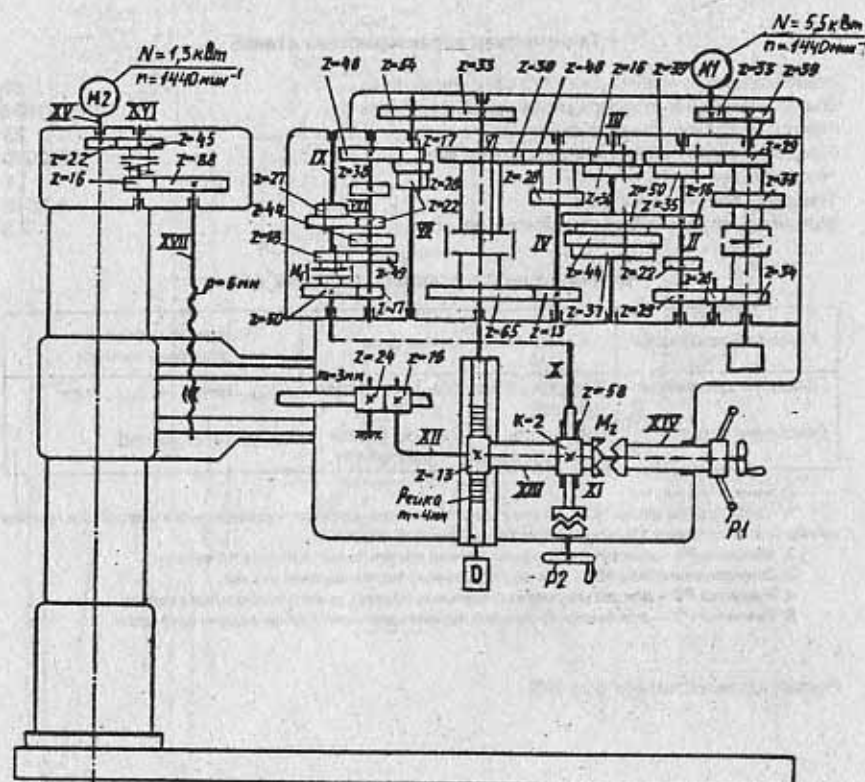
Кинематическая схема радиально-сверлильного станка мод. 2М55
